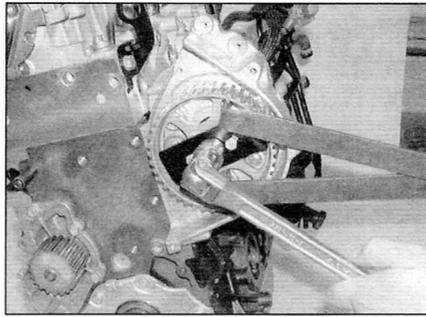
, б. Установив съемник, придержите зубчатый шкив, а затем отверните гайку крепления зубчатого шкива, чтобы отделить шкив от вала насоса (двигатели 2.0 л)
